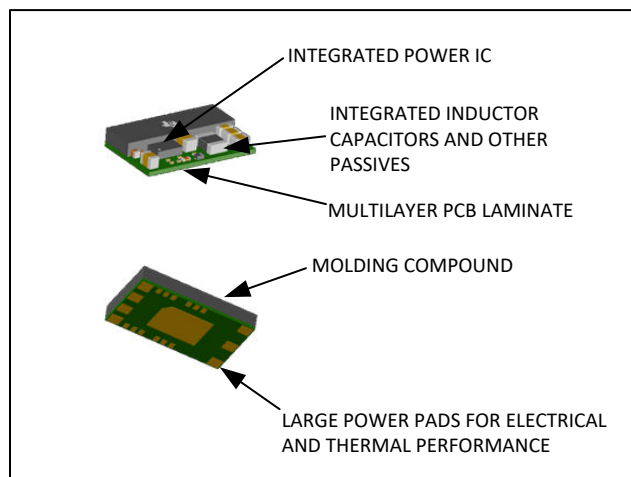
TPSM84A21 (14V、10A) 模块，采用基于 PCB 层压板的超模压 QFN 封装的
